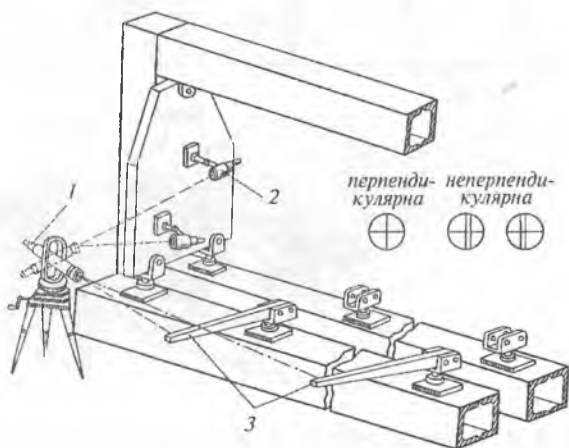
Схема проверки перпендикулярности плиты к оси приспособления: 1 — теодолит; 2 — стойки с маркой; 3 — установочная планка
